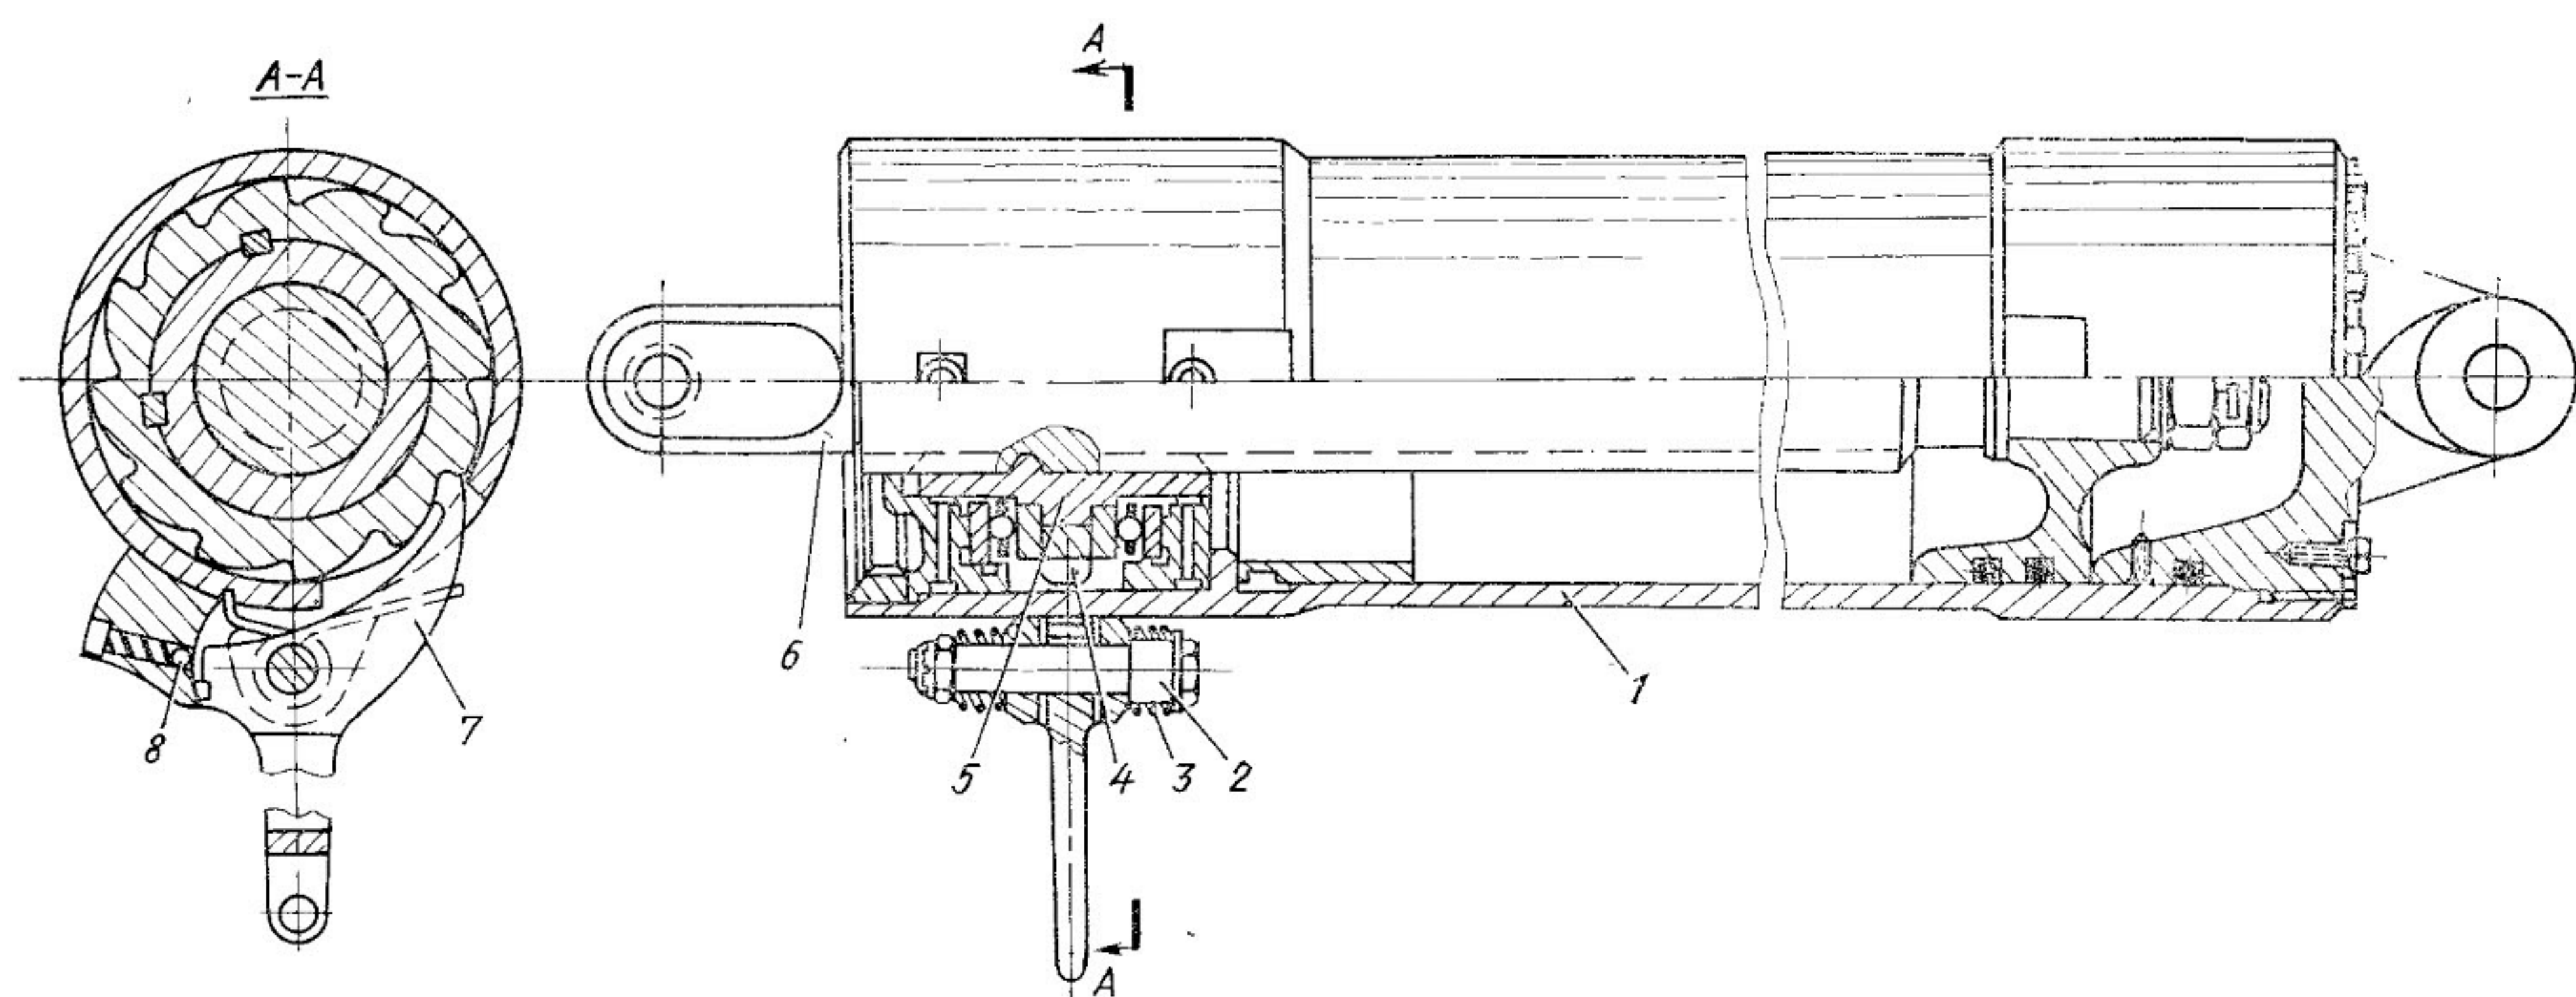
Гидроцилиндр механизма наклона лестницы со стопорным устройством:
